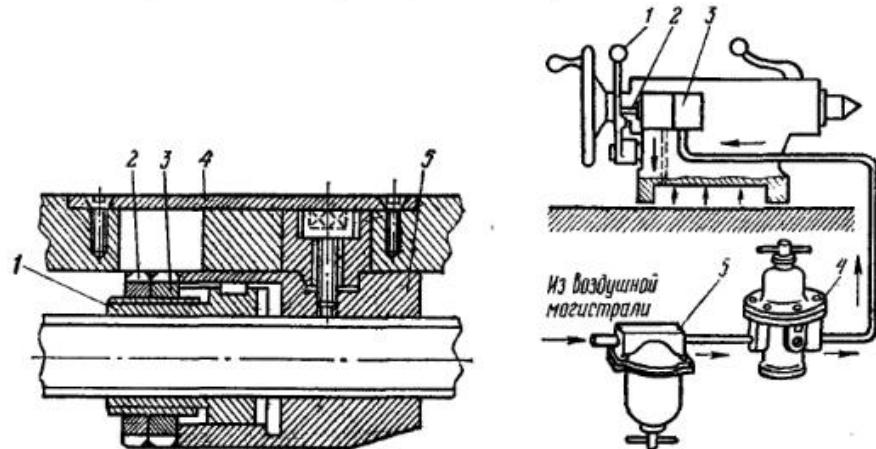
Конструкция гайки для регулирования зазора в винтовой передаче поперечных салазок суппорта станка 16К20
